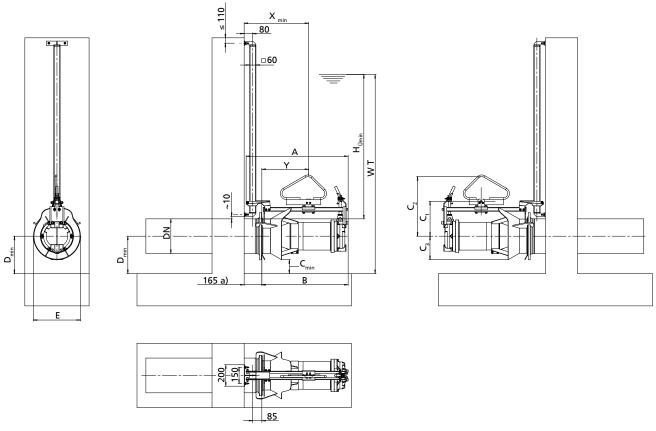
Dimensiones de Amaline 200, 300, 400 - material de la carcasa del motor: fundición gris
